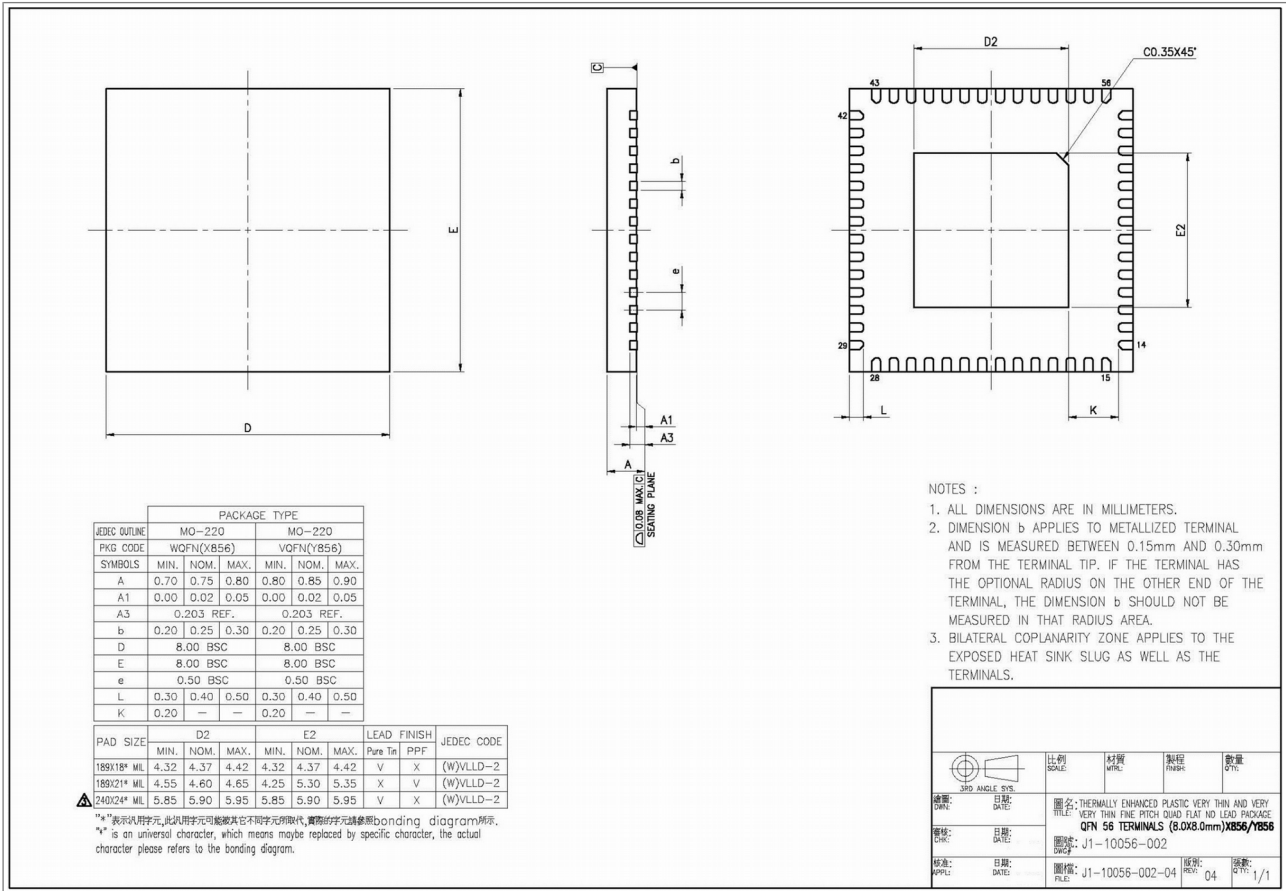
AM-IP4k QFN56 Package Dimensions
